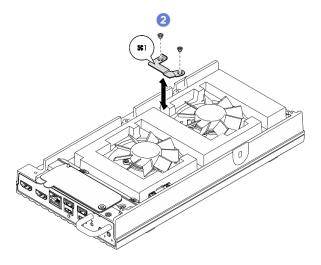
Schraubenposition der Halterung für Lüfter 1
